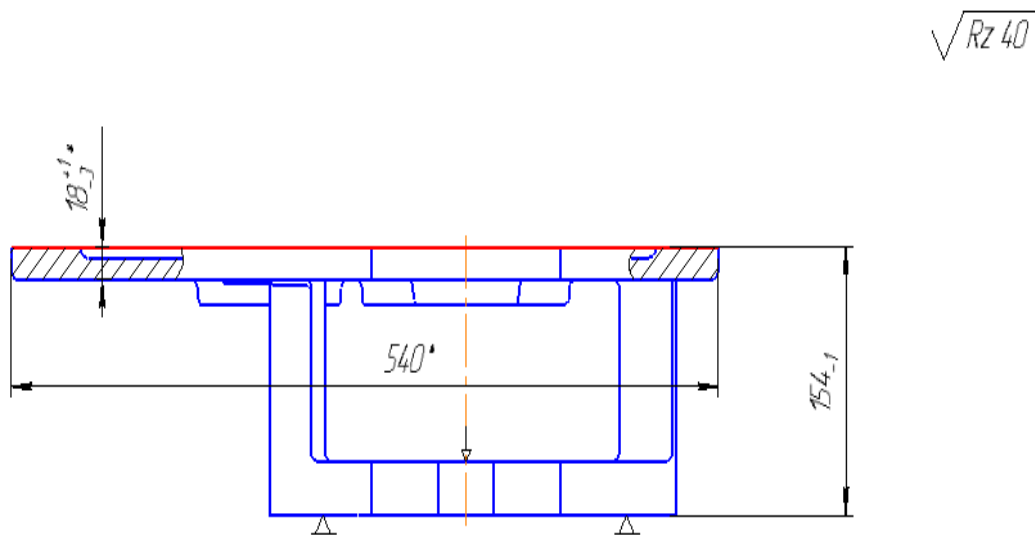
Эскиз к операции 05 – Фрезерная
